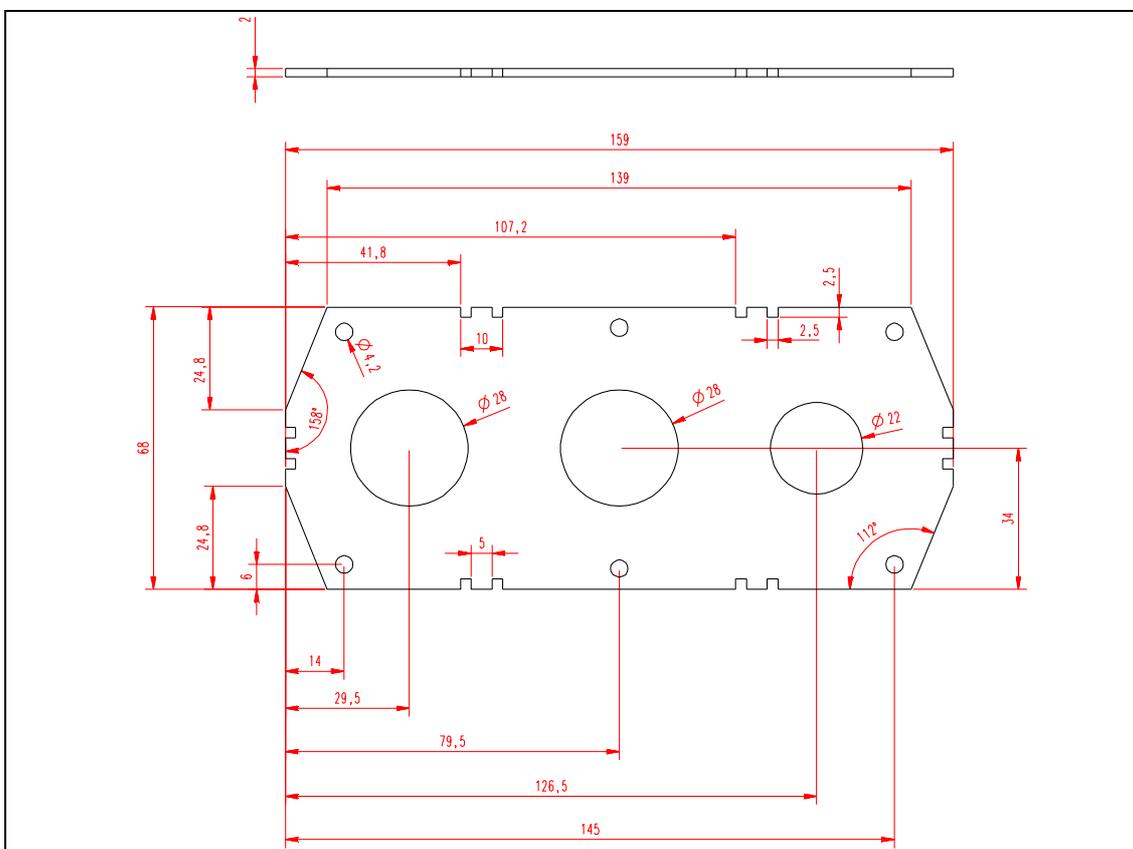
Plaque d'entrée de câble, installation MM5 UL.
